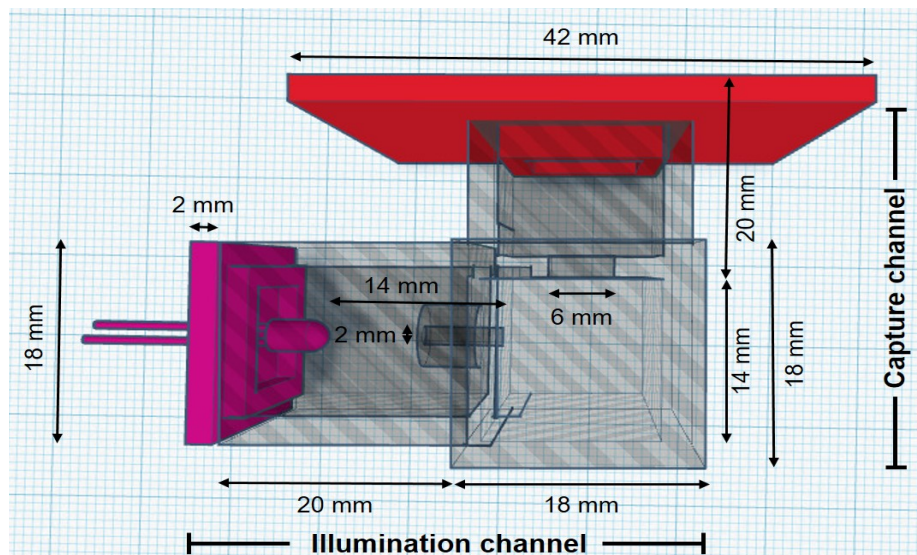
Dimensiones reales del dispositivo y detalle de las estructuras interiores.
